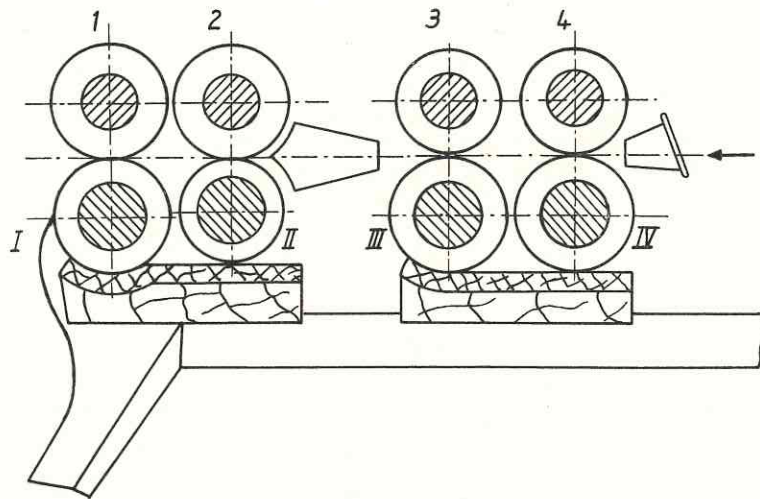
Flyer, Hochverzugsstreckwerk (Zweizonenstreckwerk)
